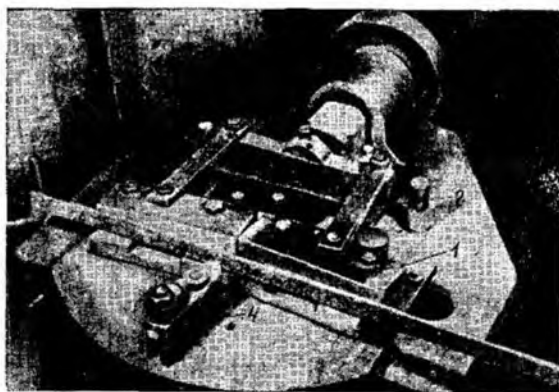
Приспособление для гнутья фланцев прямоугольного сечения
